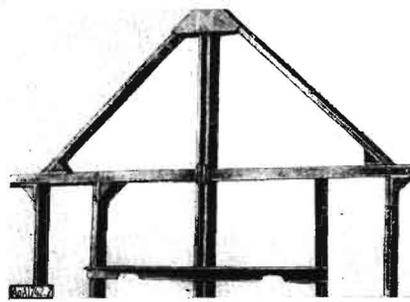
Rahmenkonstruktion in schweißgerechter Ausführung
